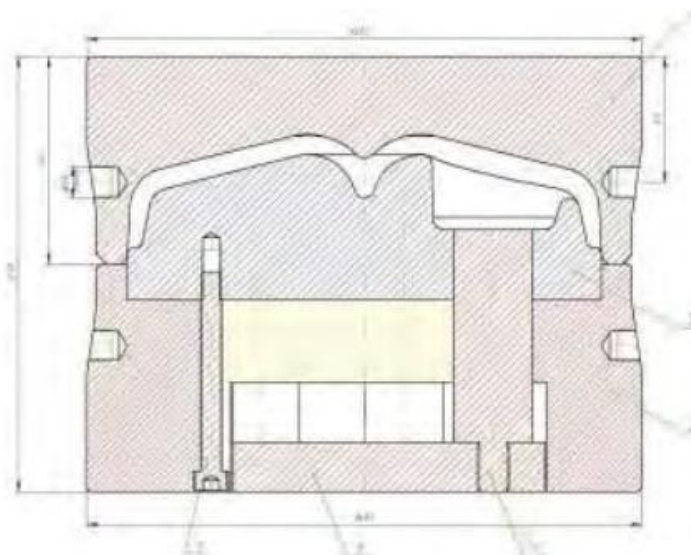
Схема штампа для об'ємного штампування заготовки мідного вінця фурми:
